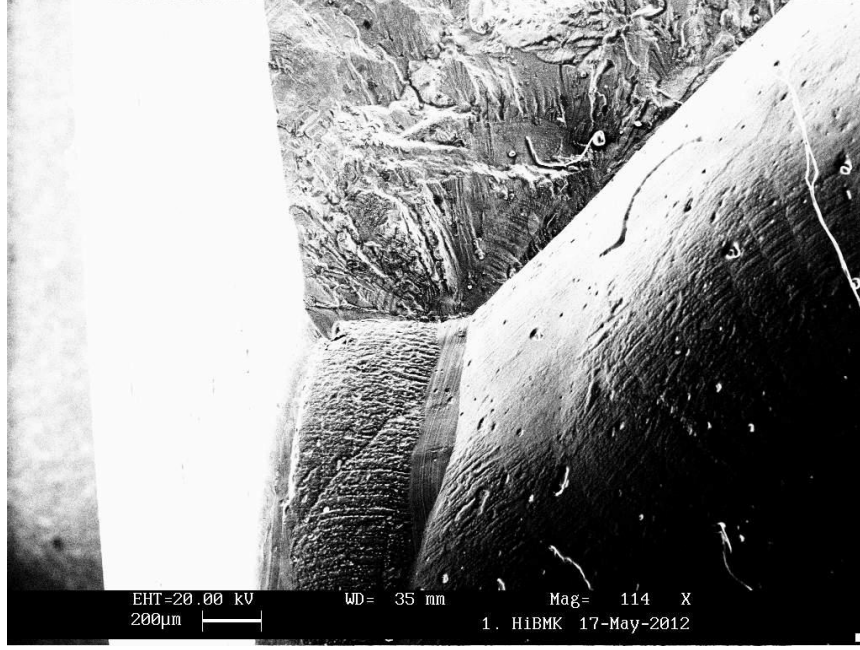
İmpeller kanat üzerinde takım izleri.
